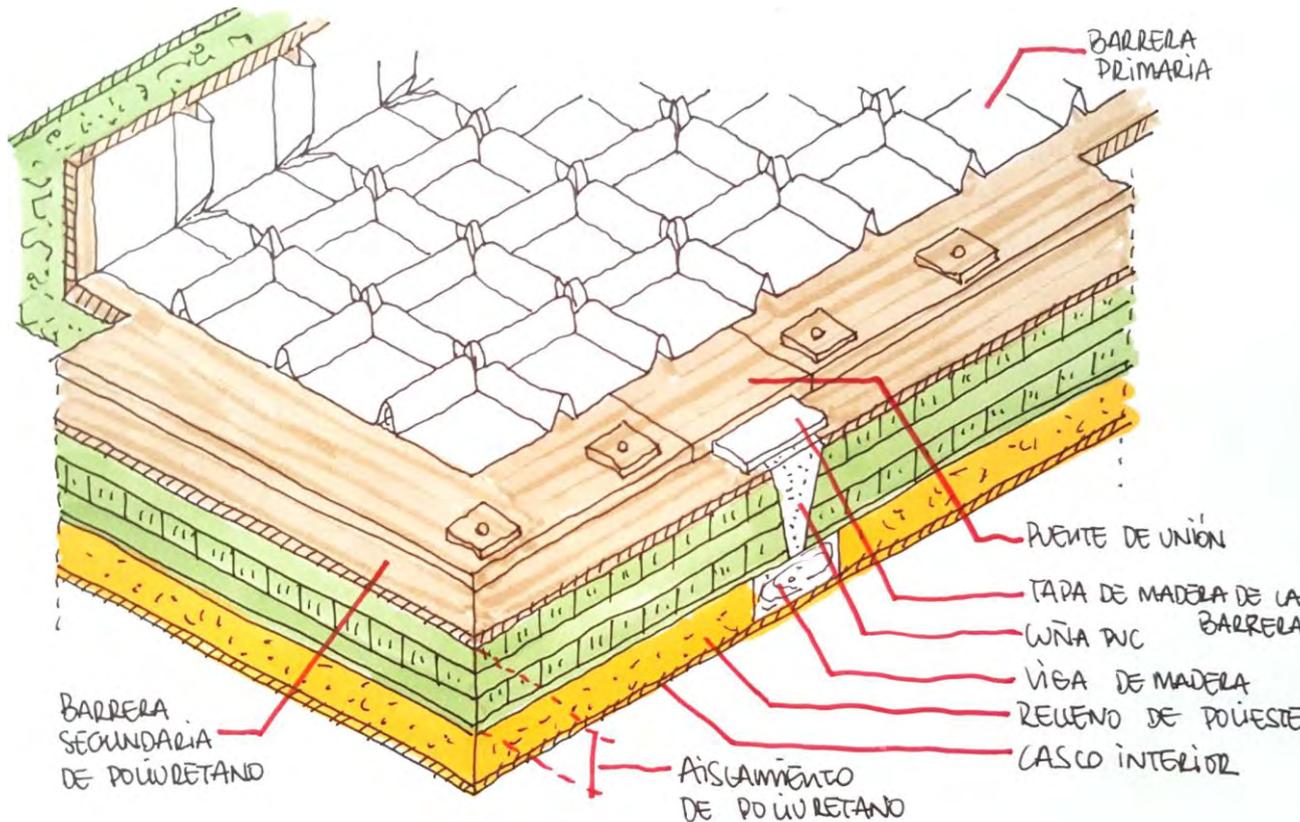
Detalle de las diferentes capas y barreras del sistema Technigaz Mark III. Obsérvese el aislamiento de Poliuretano. Fuente: elaboración propia.
